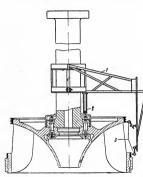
Приспособление для проверки концентричности лабиринтиых колец.
